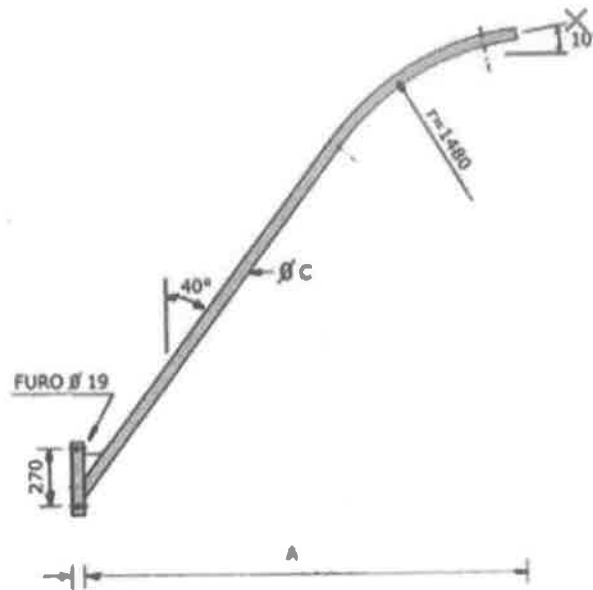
Braço de Iluminação Pública Convencional de 03 metros
